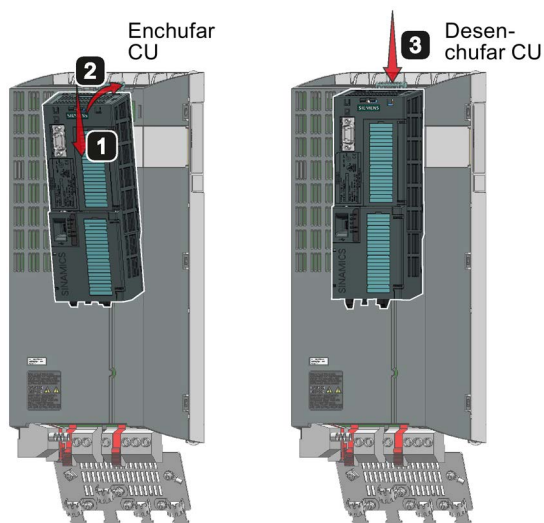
Montaje (izquierda) y desmontaje (derecha) de la Control Unit
